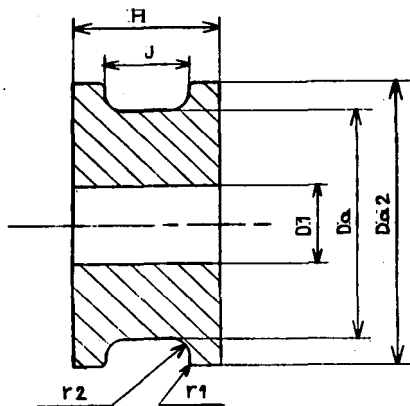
Vista en corte del diseño del rodillo exterior .
